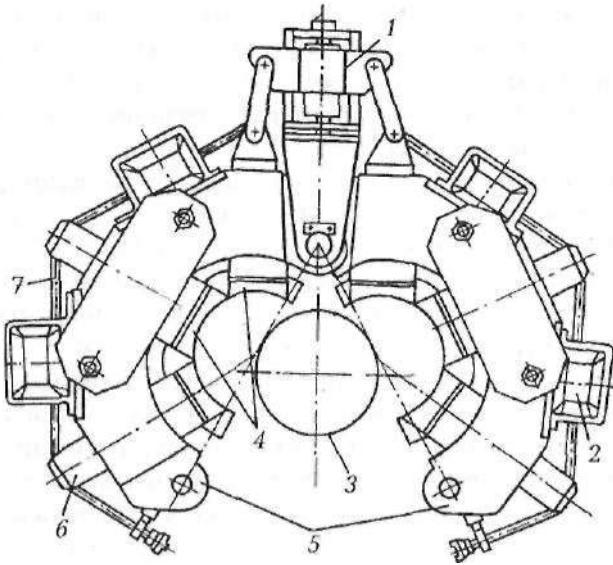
Схема механизма зажатия сварочной машины К-805:
